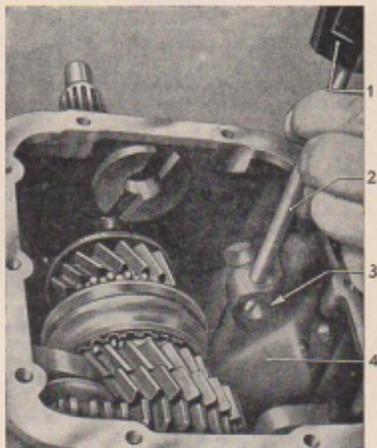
Verschlußstopfen aus Bohrung für Ganganfertigung herausschlagen
